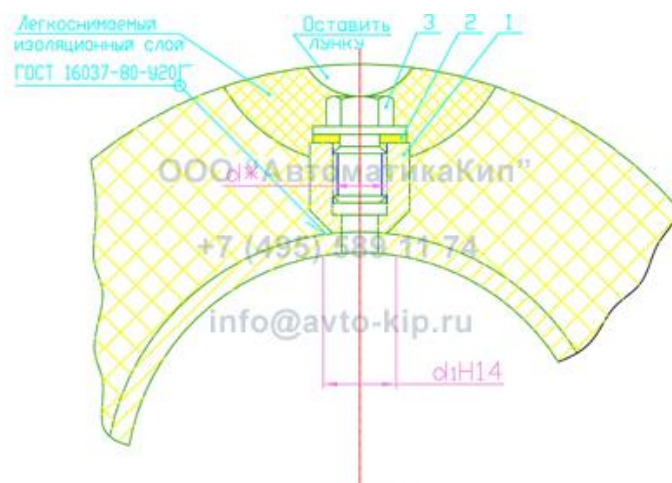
Закладная конструкция ЗК4-1-1-95
